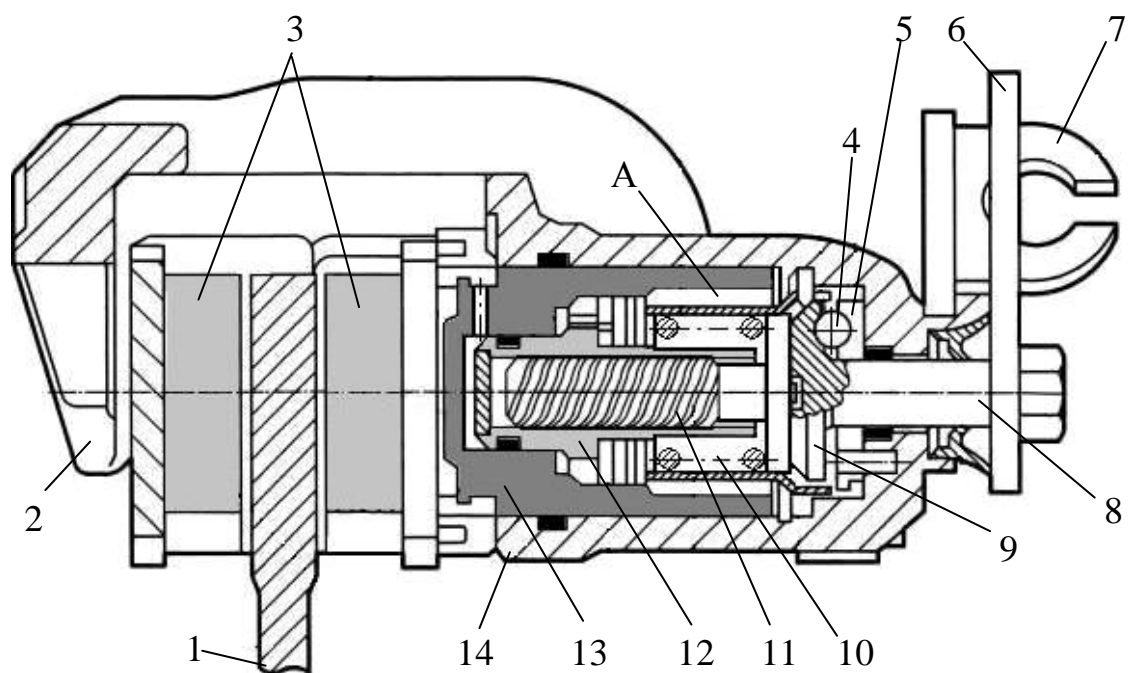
Конструкция механизма стояночного тормоза: 1 – тормозной диск; 2 – плавающая скоба; 3 – тормозные колодки; 4 – шарик; 5 – кольцо; 6 – рычаг; 7 – кронштейн крепления оплетки приводного троса; 8 – вал; 9 – пластина; 10 – пружина; 11 – винт; 12 – гайка; 13 – поршень; 14 – рабочий тормозной цилиндр; А – полость гидроцилиндра тормозного механизма рабочей тормозной системы
